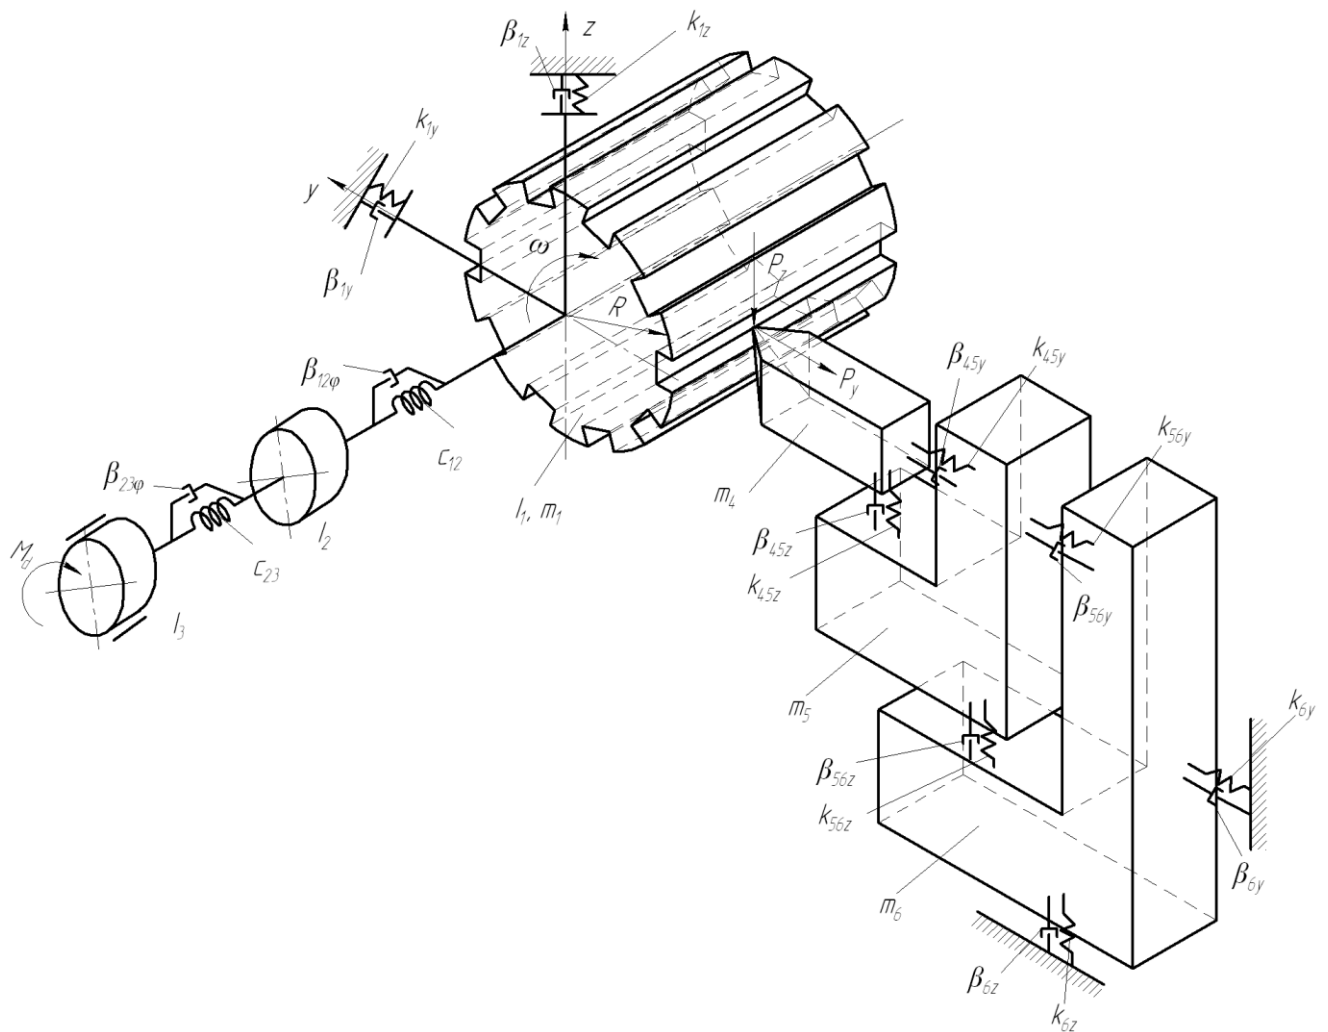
Розрахункова схема еквівалентної багатомасової системи для дослідження динаміки процесу токарної обробки перервної циліндричної поверхні
